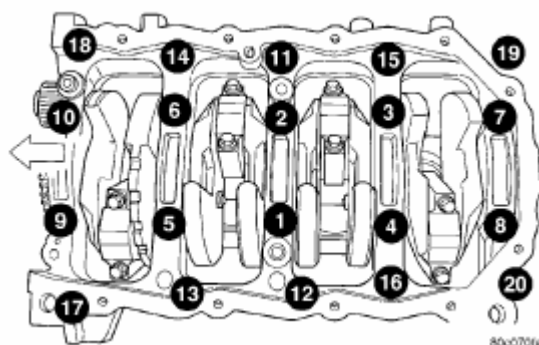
Порядок затяжки болтов крышки коренных подшипников.
